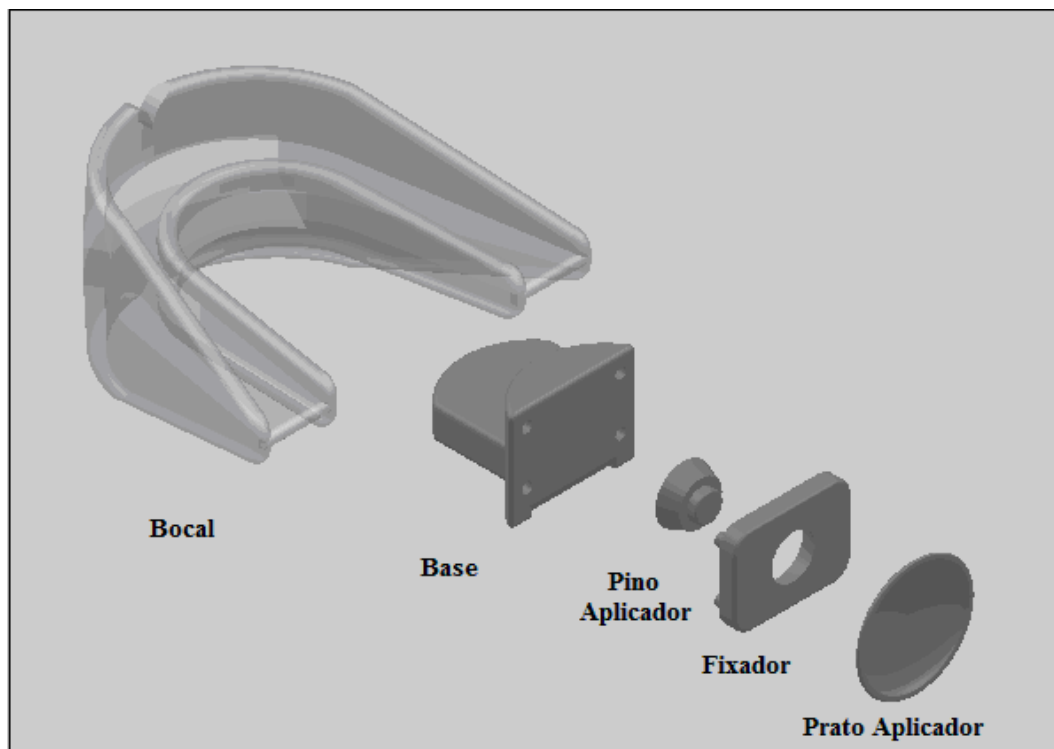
Vista isométrica exibindo o posicionamento entre bocal, base, fixador e aplicador
